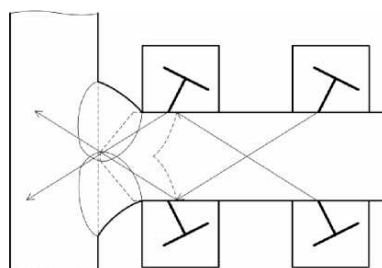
Схема контроля тавровых сварных соединений прямыми лучами
